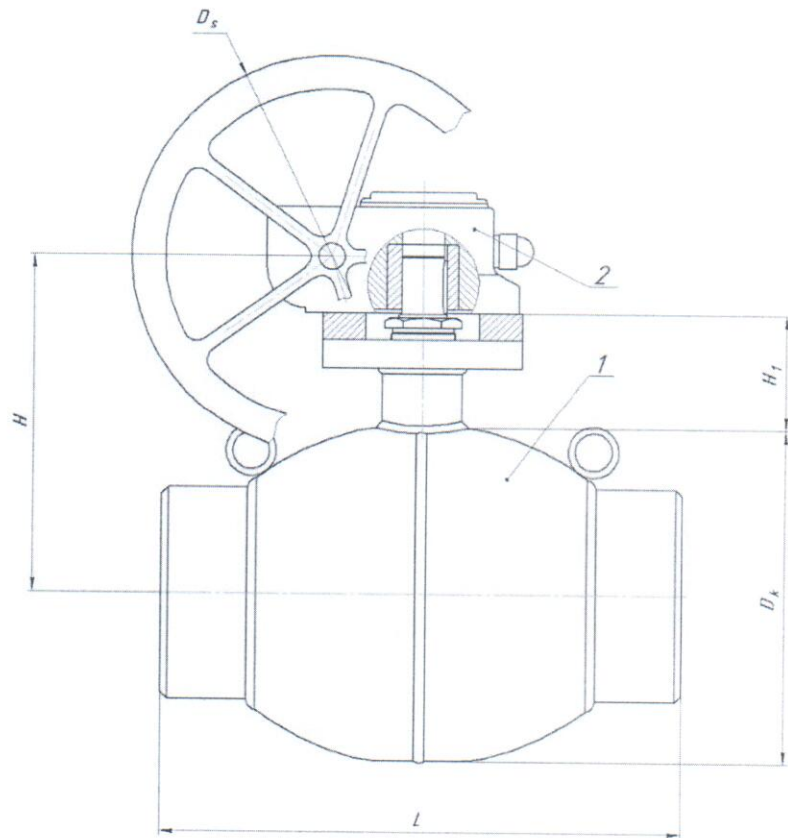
Кран шаровой цельносварной под приварку с редуктором
